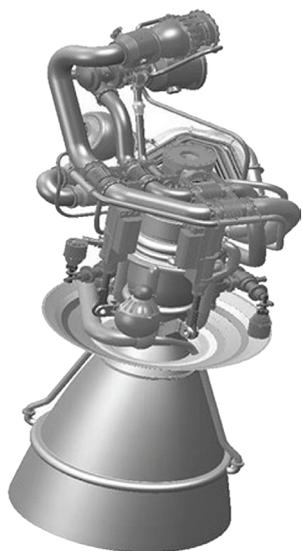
Компьютерный макет двигателя РД0162 с дожиганием генераторного газа
